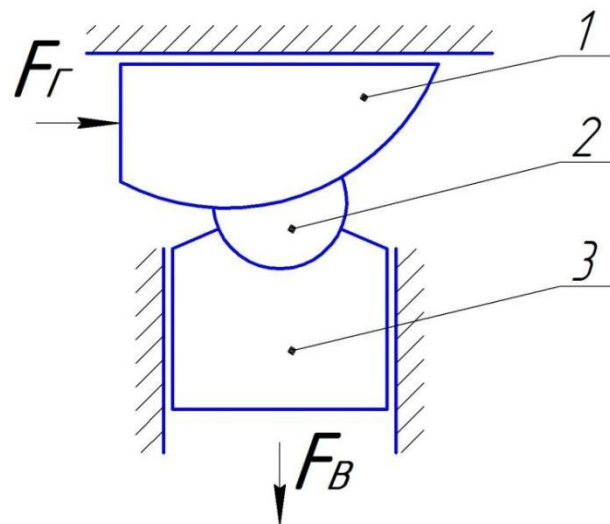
Схема клиношарнирного механизма с выпуклым клином [9] (1 – клин; 2 – шарнир; 3 – ползун)
